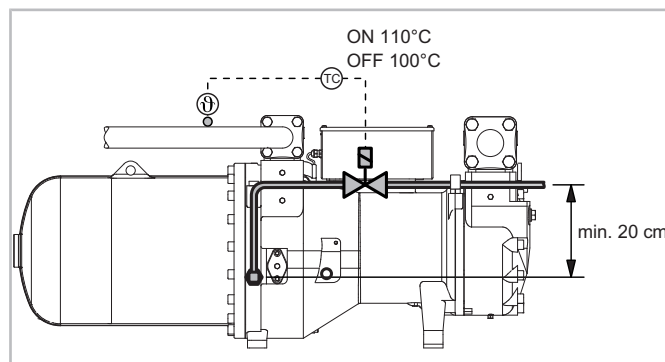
Rohrführung für Kältemitteleinspritzung (LI) mit Kältemittelspritzventil
